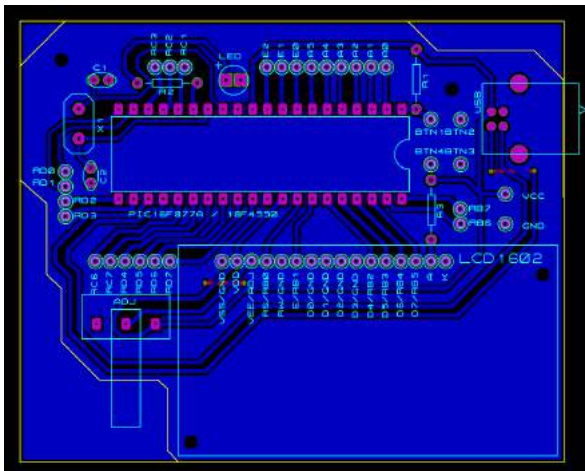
Diseño PCB de la tarjeta para el PIC16F877A.
